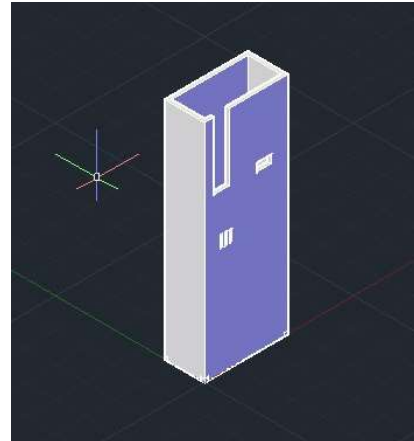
, Diseño de protección para la PCB madre impreso en ABS
